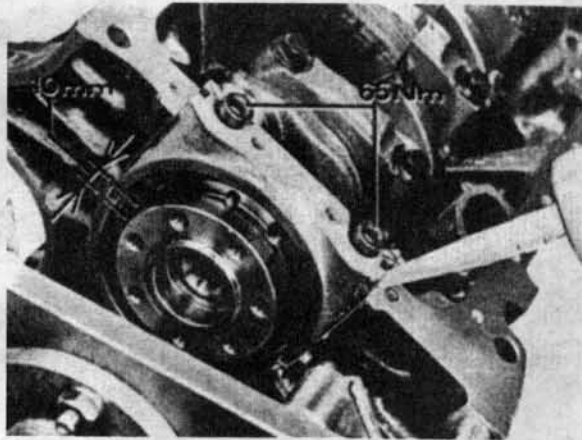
Установка крышки 1-го коренного подшипника коленвала
